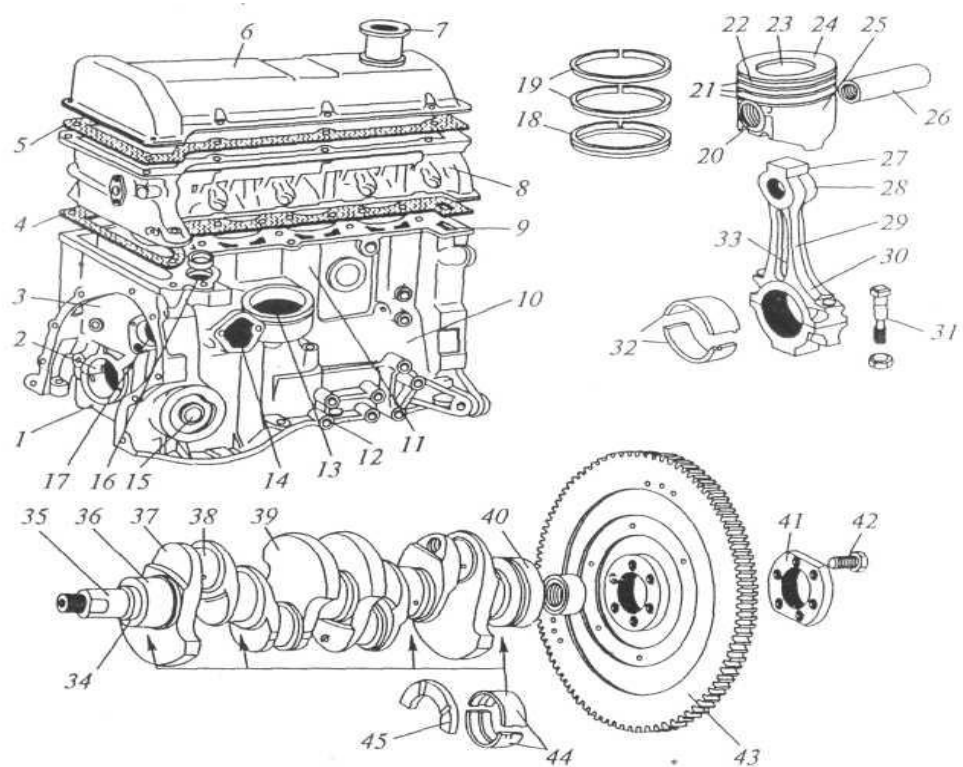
Кривошипно-шатунный механизм двигателей легковых автомобилей ВАЗ:
